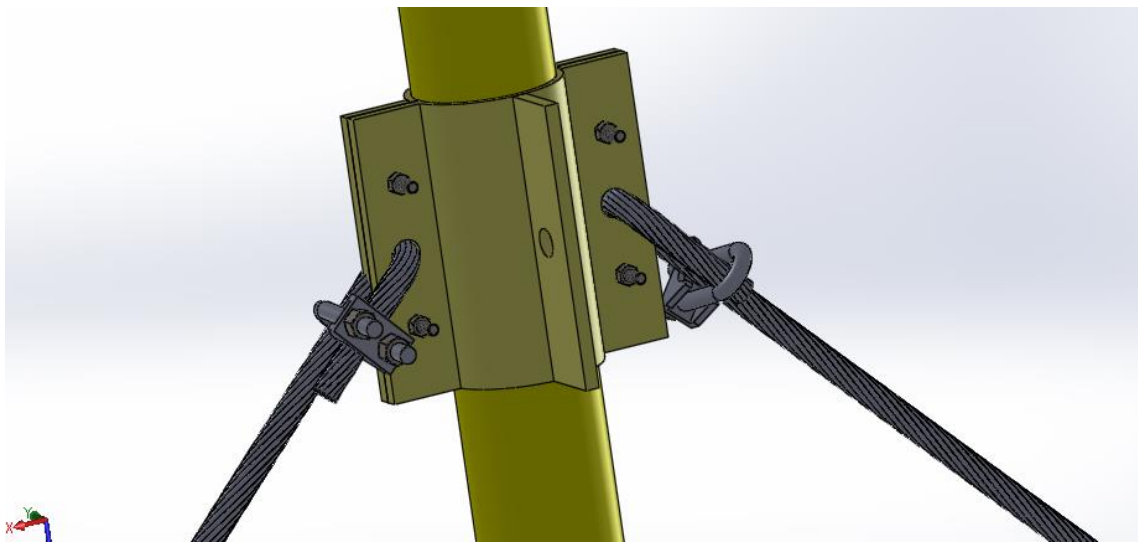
Assemblage mât – câbles par des manchons et serre câble.
